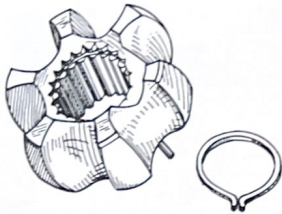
Parte inferior de la junta homocinética-fija, con las gargantas para las bolas visibles en su exterior y su arandela.
